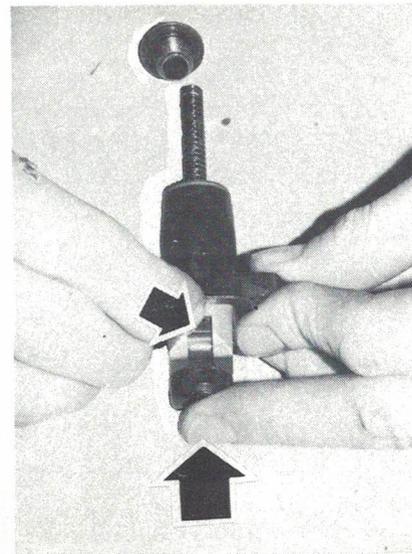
Repousser le poussoir du tendeur (Photo RMT)
